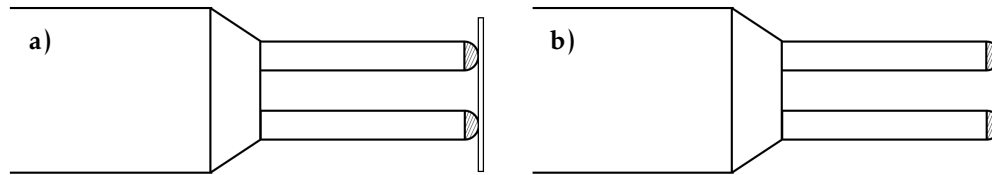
a) Posición hilo-soldadura antes de soldar y b) Posición hilo-soldadura después de soldar.
